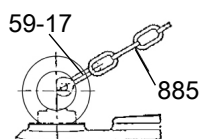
Befestigung der Kette mit Schäkel an der Ringschraube
